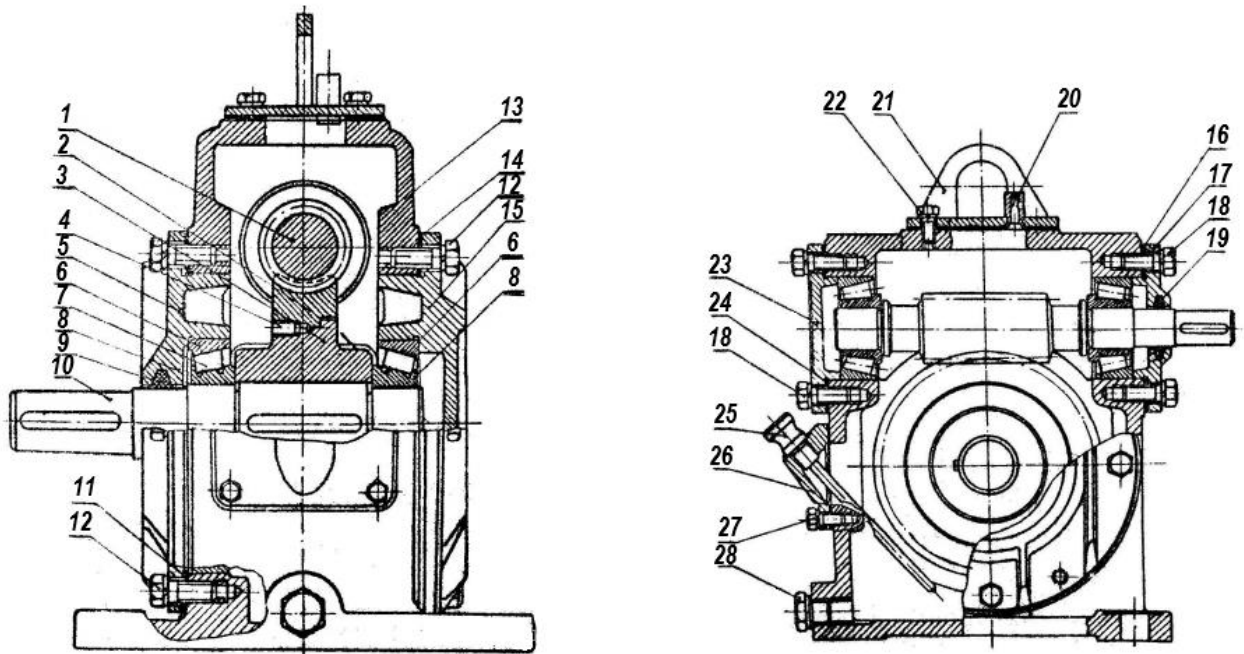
Конструкція одноступічного черв'ячного редуктора Ч-63 з основними деталями:
